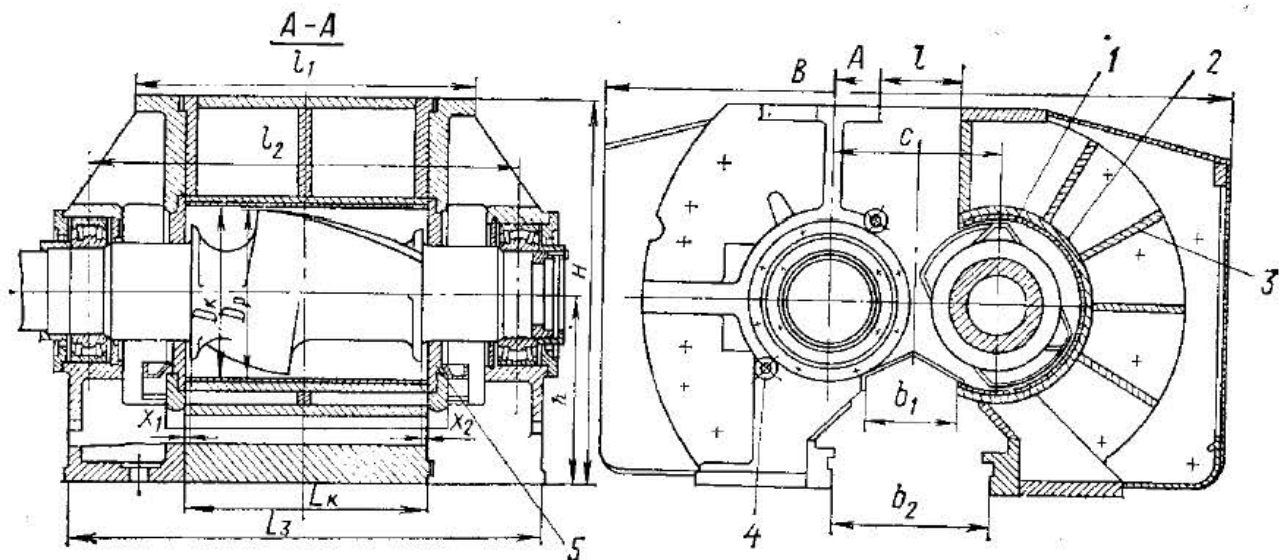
Конструкція робочої змішувальної камери гумозмішувача:
